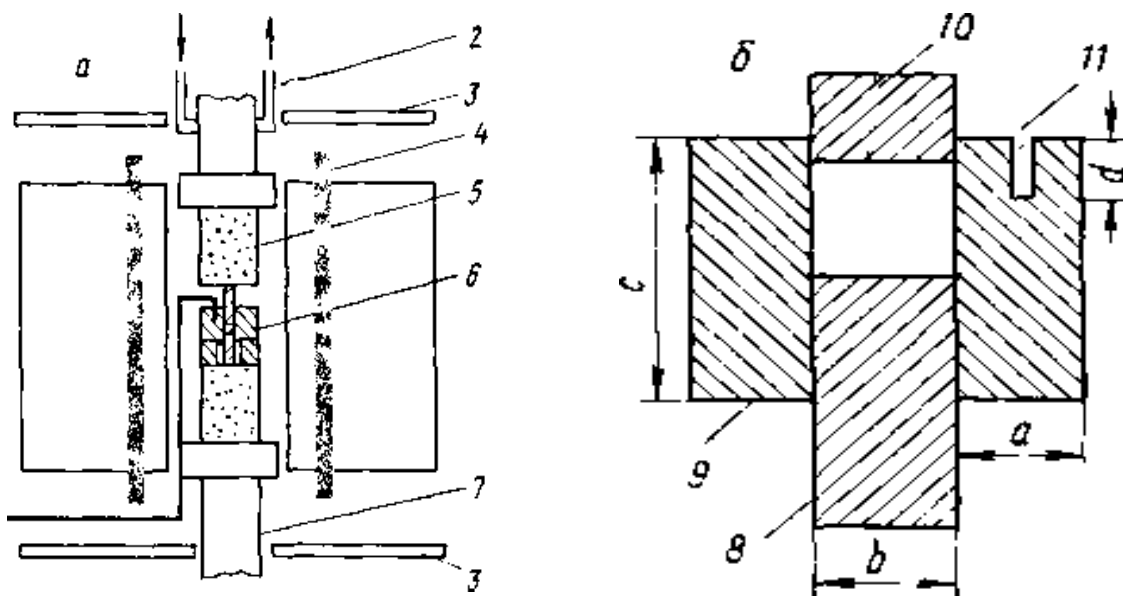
Схема установки (а) и прессформы (б) для горячего прессования: 1 — термопара; 2 — система водного охлаждения; 3 — металлическая теплоотражающая плита; 4 — нагревательный силистовый стержень; 5 — корундовый стержень для передачи давления; 6 — прессформа; 7 — подвижный пуансон; 8 — нижний пуансон; 9 — корпус формы; 10 — верхний пуансон; 11 — щель для термопары
